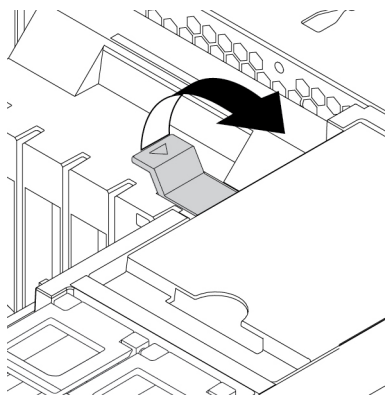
Abrindo a trava no conjunto do ventilador frontal
